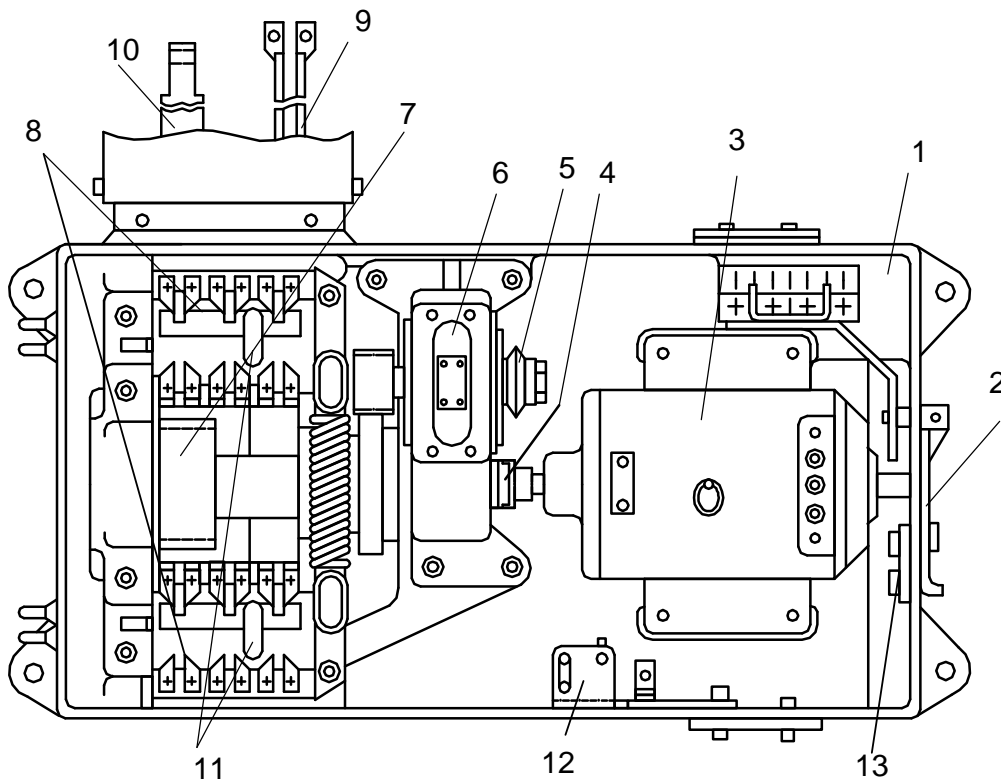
Стрілочний привод типу СП-6 (вигляд зверху):
